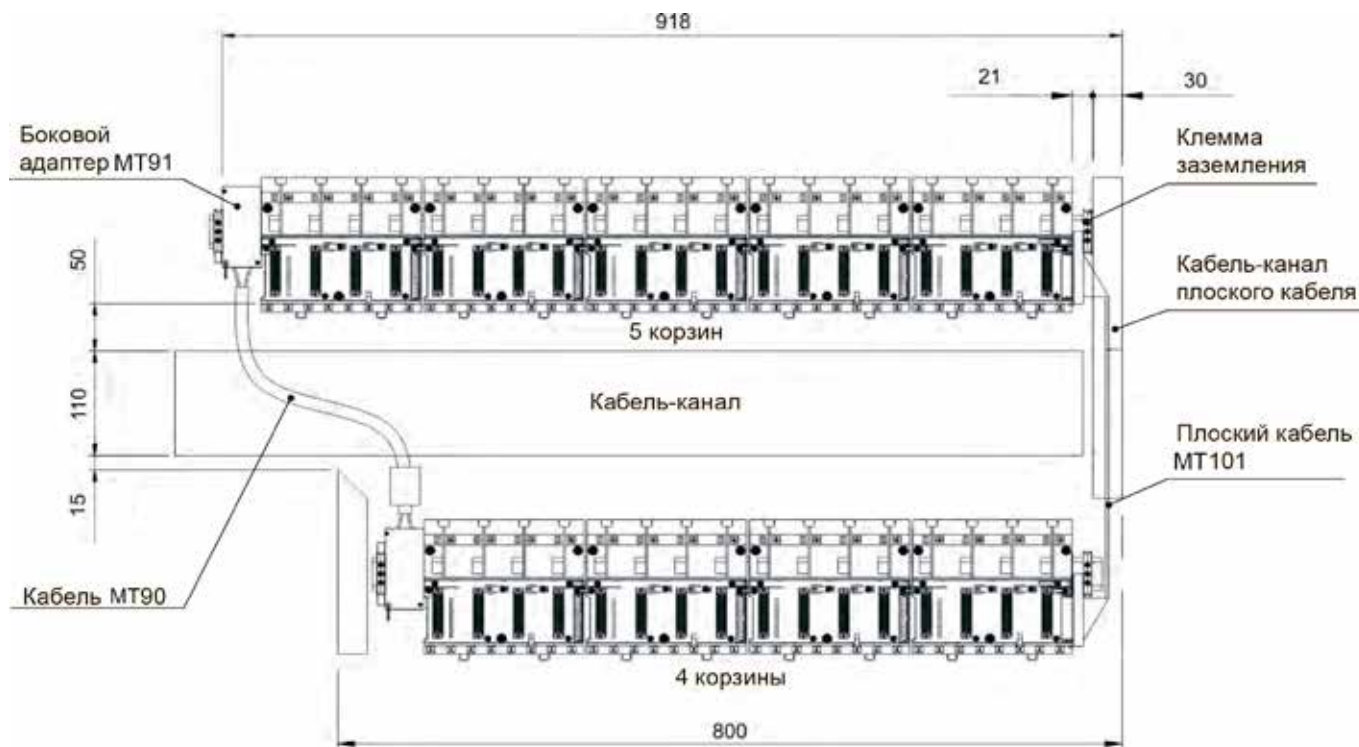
Габаритные чертежи стойки MT93 и модулей
